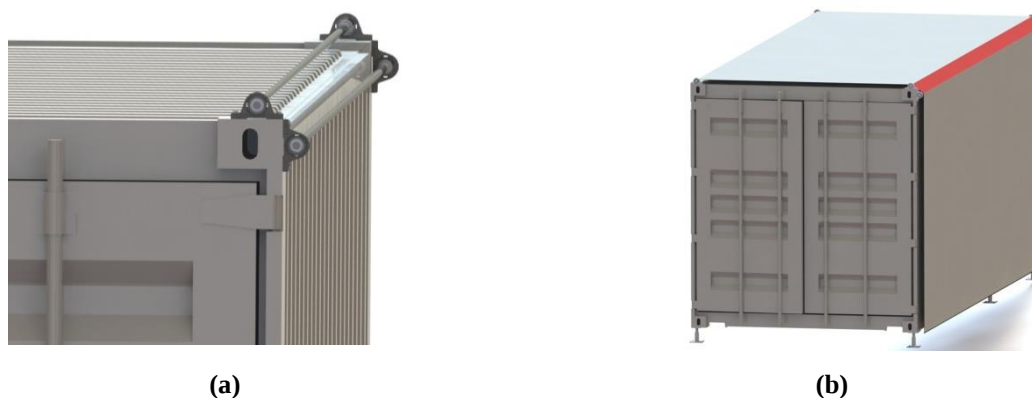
Cortina de sombreamento. (a) Suportes e varões instalados no container, (b) Mecanismo montado em um container.
